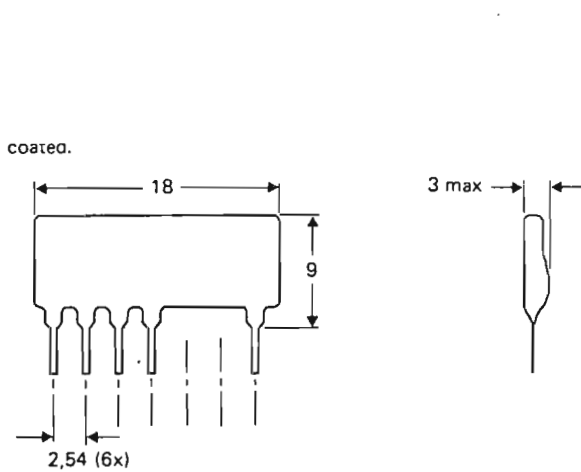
Dimensioni d'ingombro e collegamenti elettrici (in mm) dell'OM 350,
